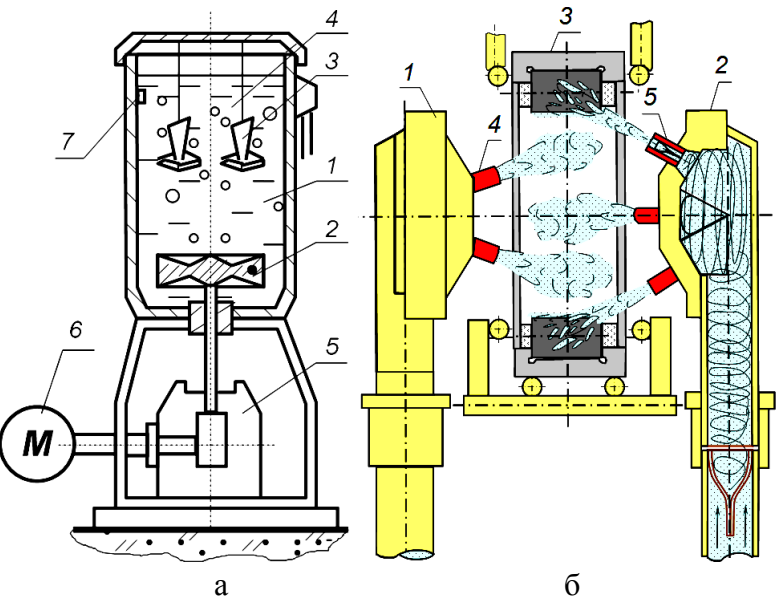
Варианты разработанных установок: а – схема установки для промывки деталей при погружении в кавитирующую жидкость; б – схема устройства для промывки крупногабаритных подшипников: 1, 2 – струйно-кавитационные головки; 3 – промываемый подшипник; 4 – сопла; 5 – кавитатор
